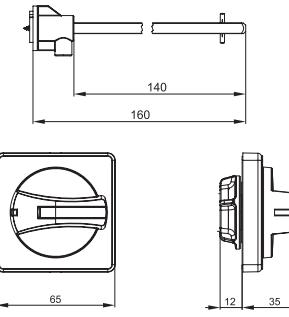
Габаритные и установочные размеры рукояти выносной / Figure 4 – Overall and mounting dimensions of the extended handle / 4 сурет – Шығармалы тұтқының габариттік және орнату өлшемдері
